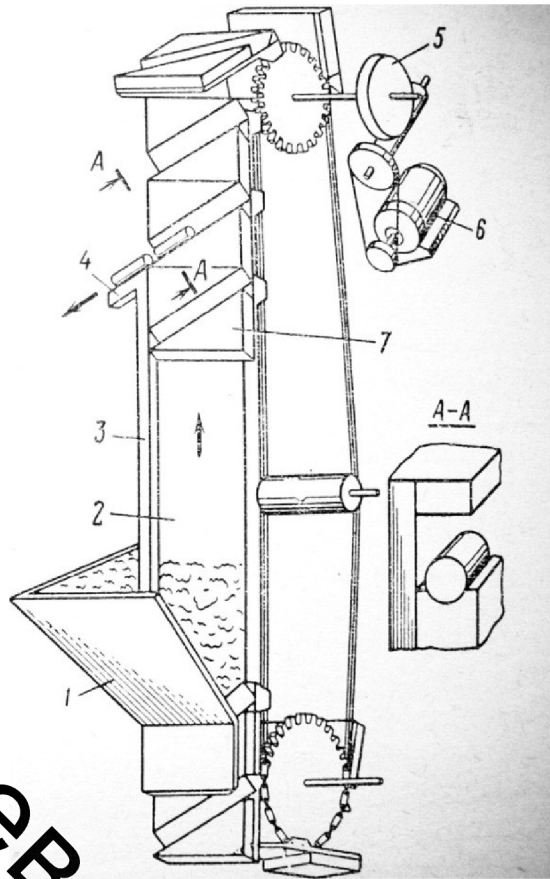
Бункерний завантажувальний пристрій елеваторного типу
